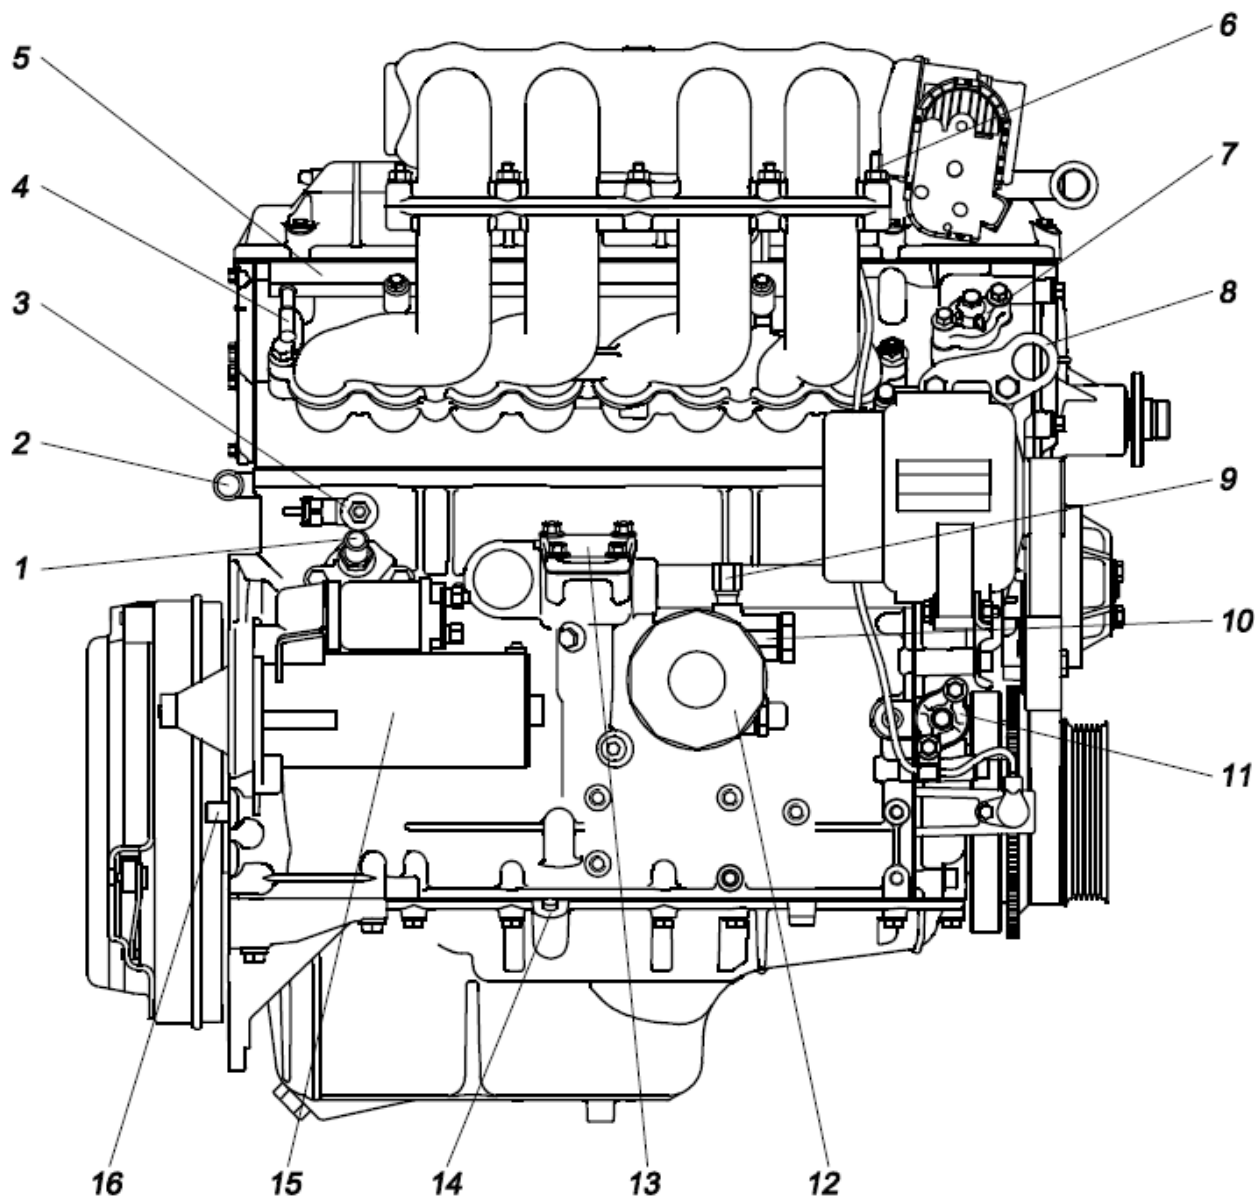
Вид слева двигателя ЗМЗ-40904.10:
